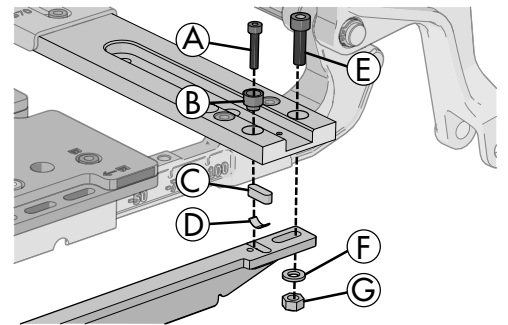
Die hintere Montage der Stellvorrichtungshalterung für die Rückenlehne.
